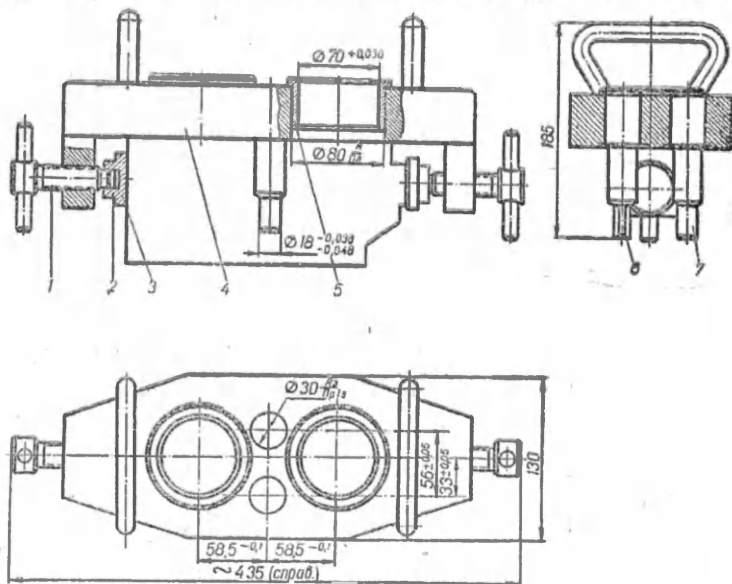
Кондуктор накладной для расточки выточек под вставки камер сгорания головки цилиндров двигателя Д-40:
